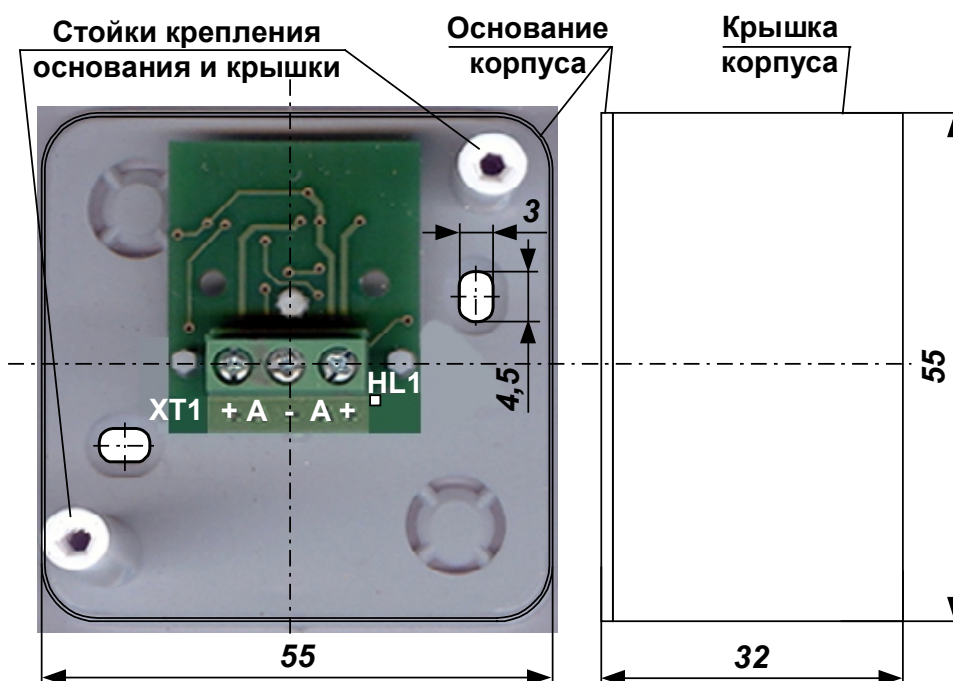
МКЗ. Внешний вид без крышки. Габаритные и присоединительные размеры
